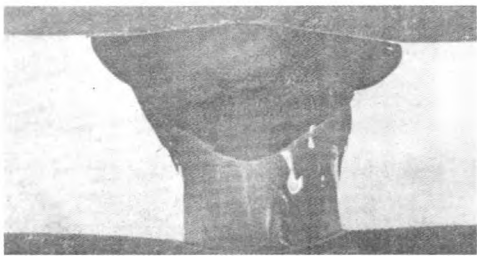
选用 HGH367 焊丝所焊试验件
